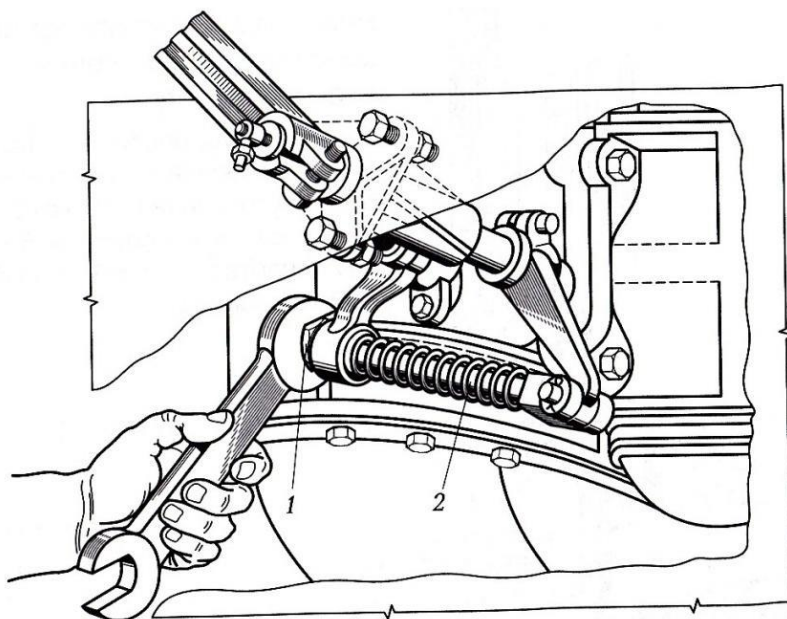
Регулировка свободного хода педали сцепления с механическим приводом:
